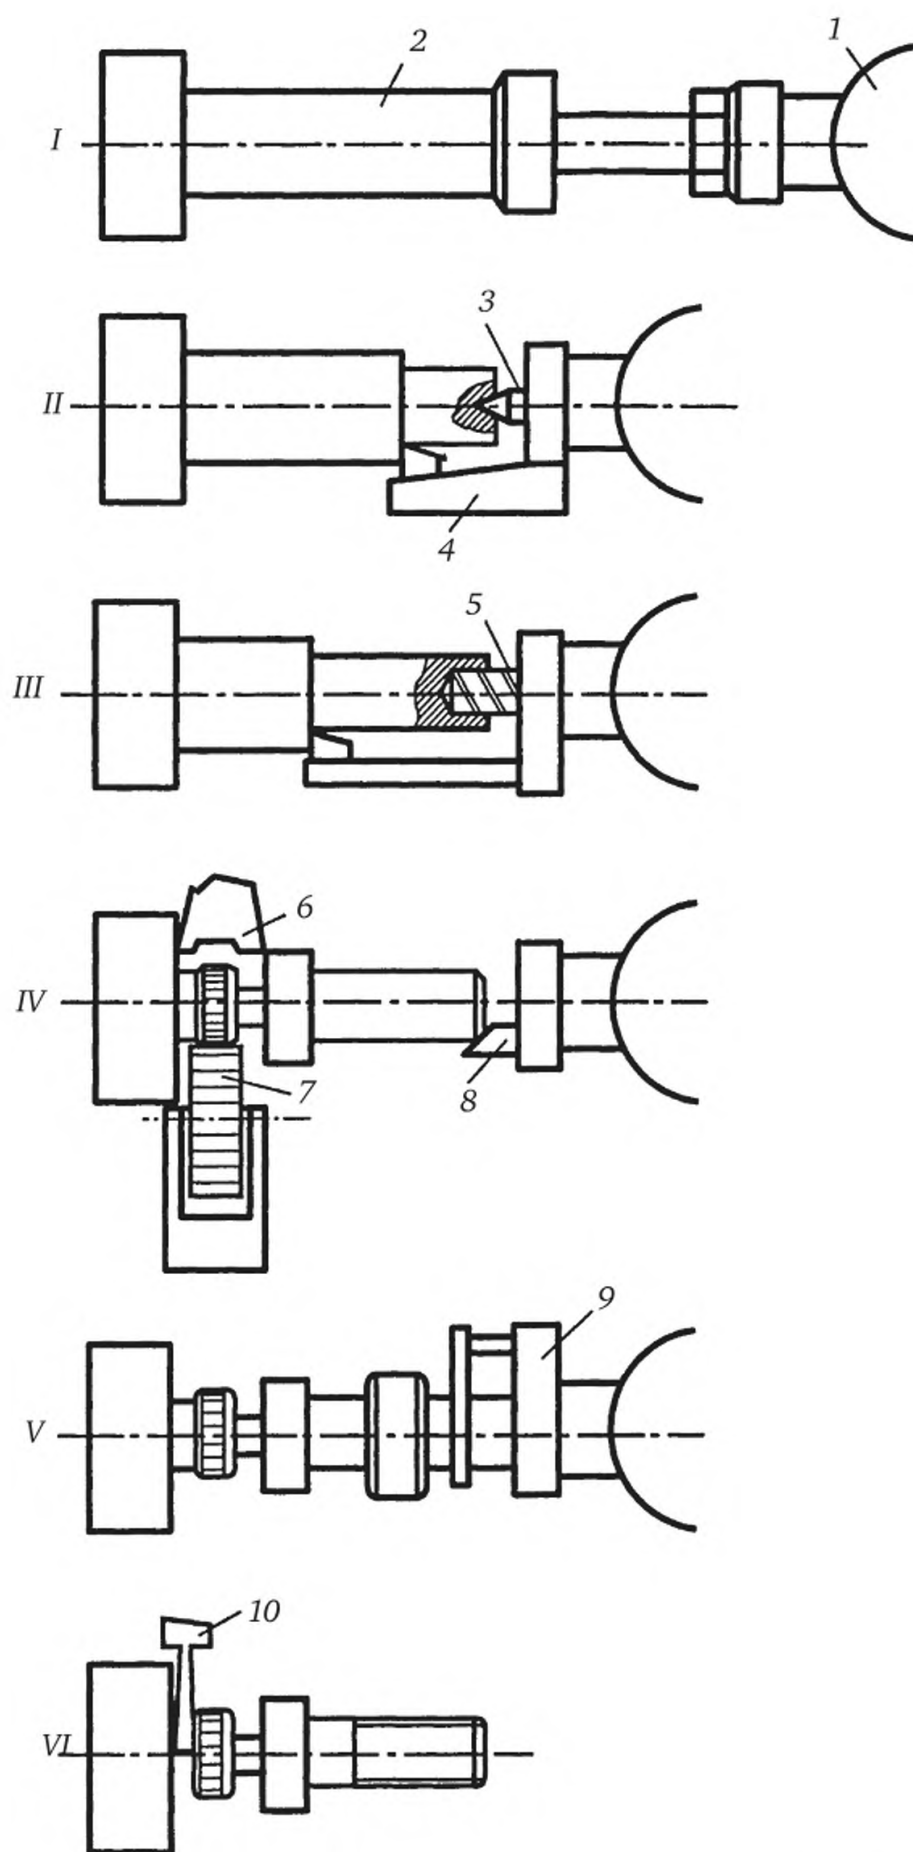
Схема обработки на токарно-револьверном автомате
